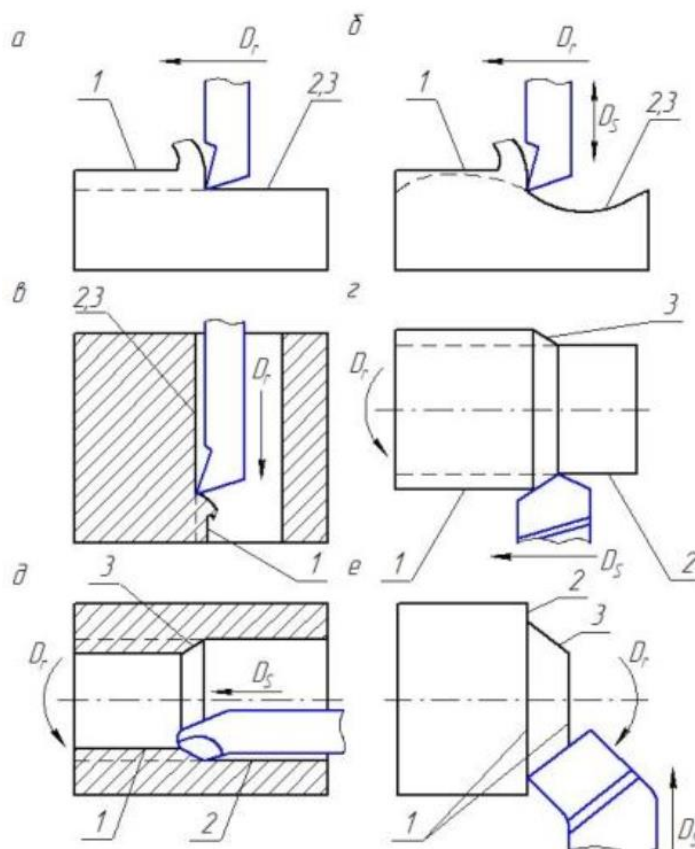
Схемы видов лезвийной обработки: а - строгание; б - строгание по копиру; в - долбление; г - обтачивание; д - растачивание; е - подрезание; 1 - обрабатываемая поверхность; 2 - обработанная поверхность; 3 - поверхность резания;  $D_r$  - главное движение;  $D_s$  - движение подачи.
